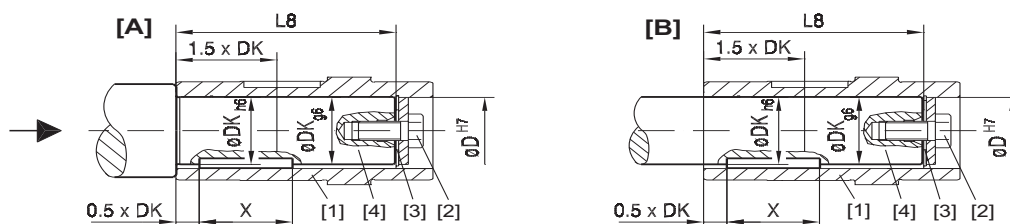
Ведомый вал с опорным выступом (A) и без опорного выступа (B)
